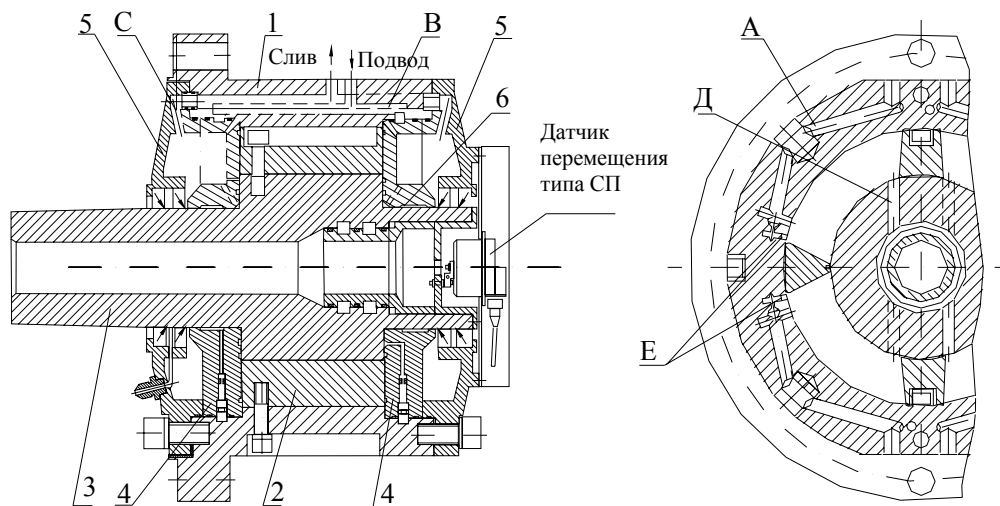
Конструктивная схема гидродвигателя типа НПМ
